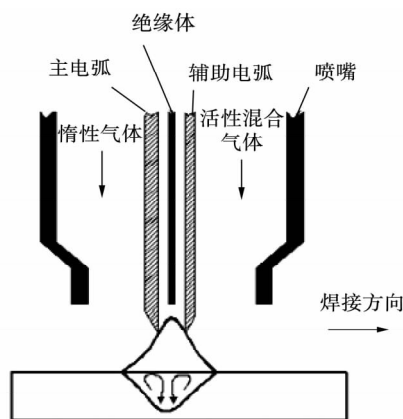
耦合电弧 AA-TIG 焊接示意图
